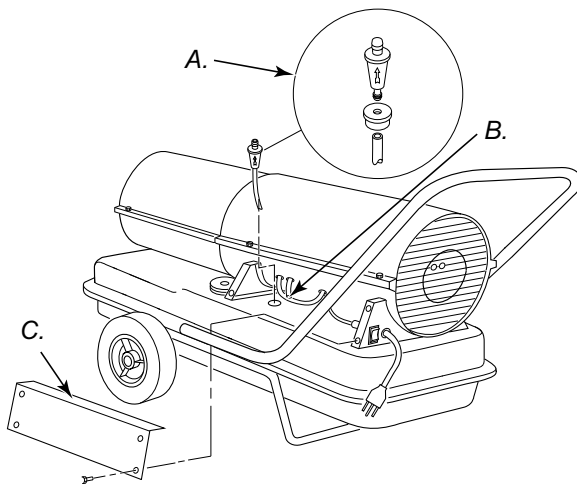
Dépose du filtre à carburant, Modèles 29 kW.
